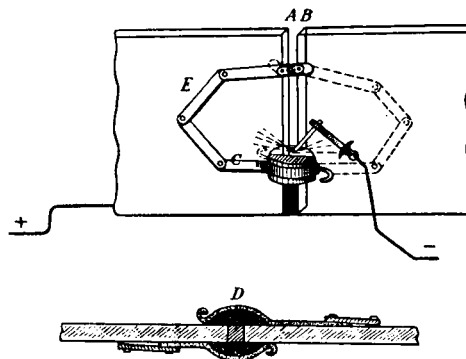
Приспособление для сварки встык вертикальных швов.
